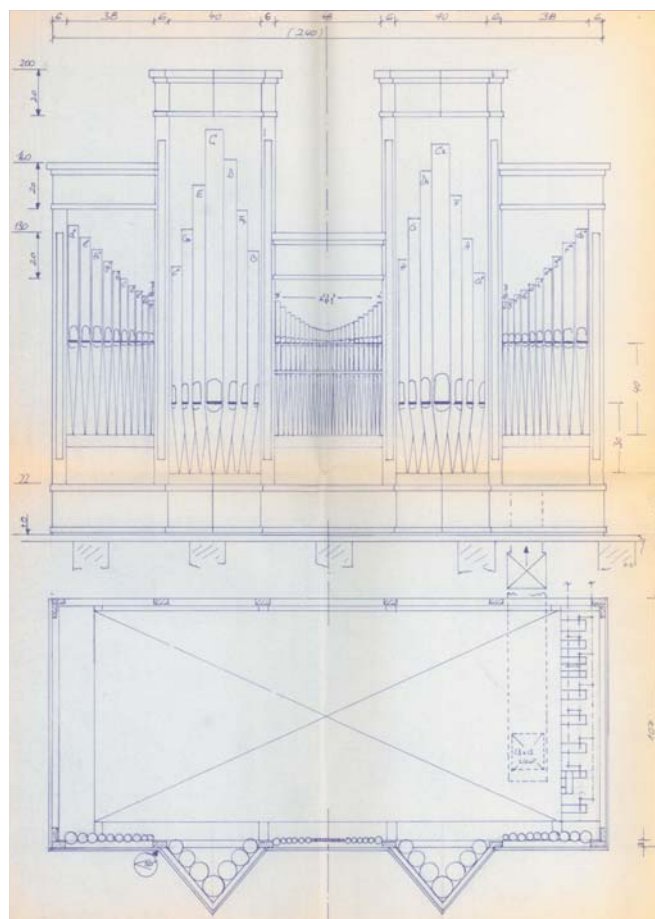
Ausschnitt Entwurf Rückpositiv Grundriss und Schnitt, Orgelbau Rensch, 17.1.1985
